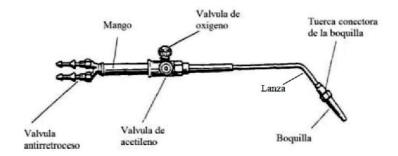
Elementos de que consta un equipo de soldadura oxiacetilénica.
